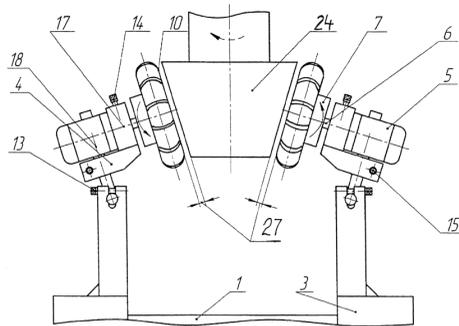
Схема применения предлагаемого устройства при обработке конической поверхности детали на вертикально-фрезерном станке
